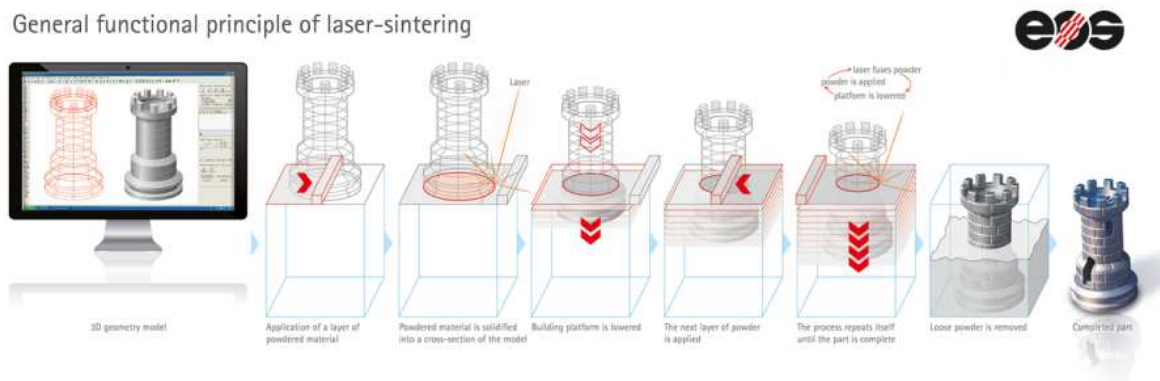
Processo do *Selective Laser Sintering* [9]
